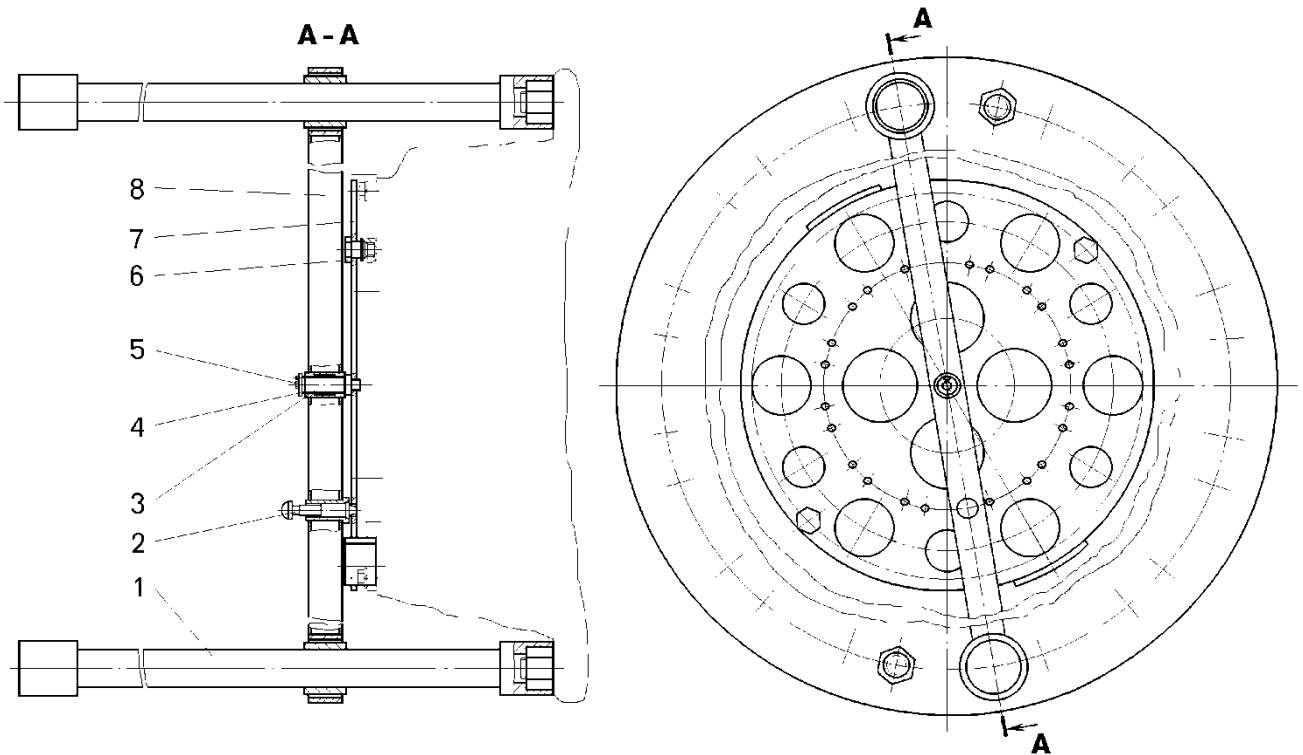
Загальний вигляд пристосування з каталожним номером 360–012, для підтримки ключа при монтажі гайок кріплення задніх коліс: 1 - ключ; 2 - фіксатор; 3 - штифт; 4 - шайба; 5, 6 - болти; 7 - диск; 8 - балка
